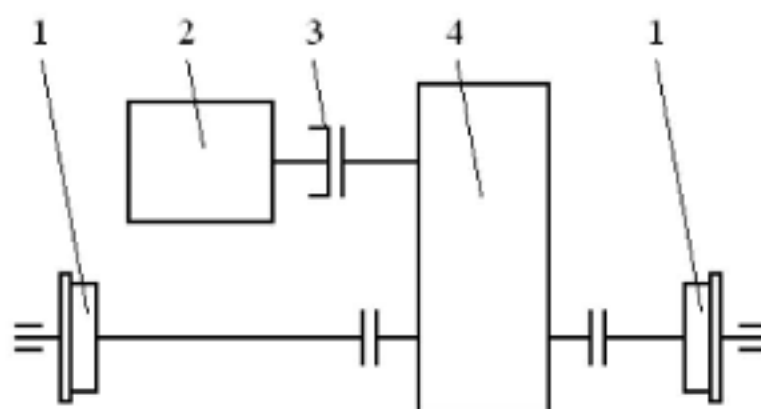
Кинематическая схема механизма передвижения тележки: 1 – ходовые колеса; 2 – электродвигатель; 3 – тормозной шкив; 4 – редуктор
